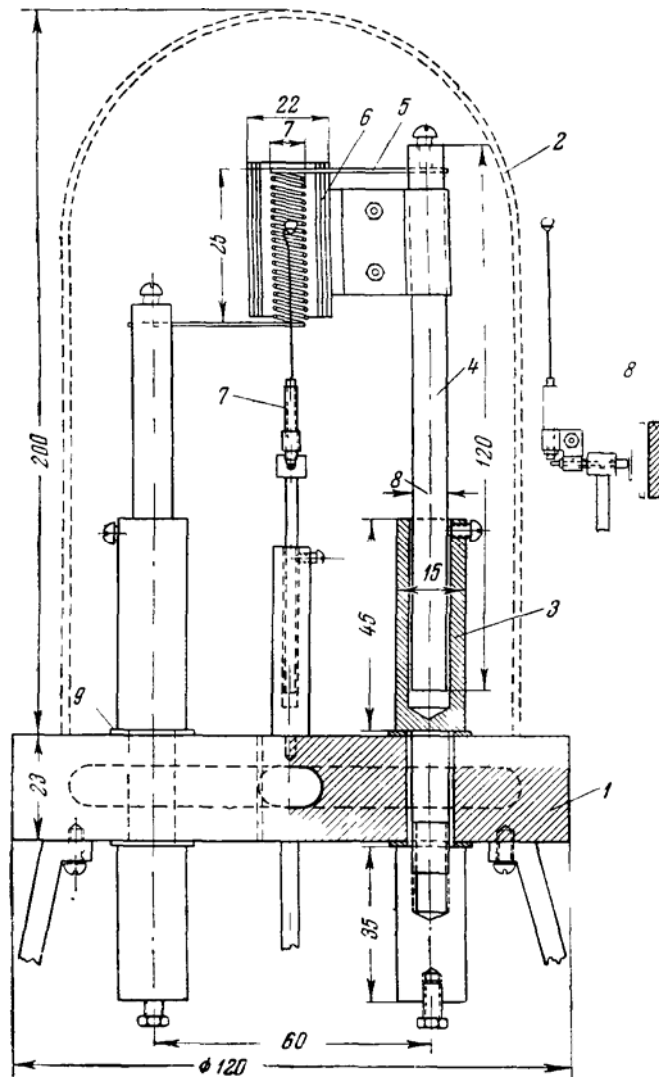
Схематический разрез закалочной микропечи на 2500°:
